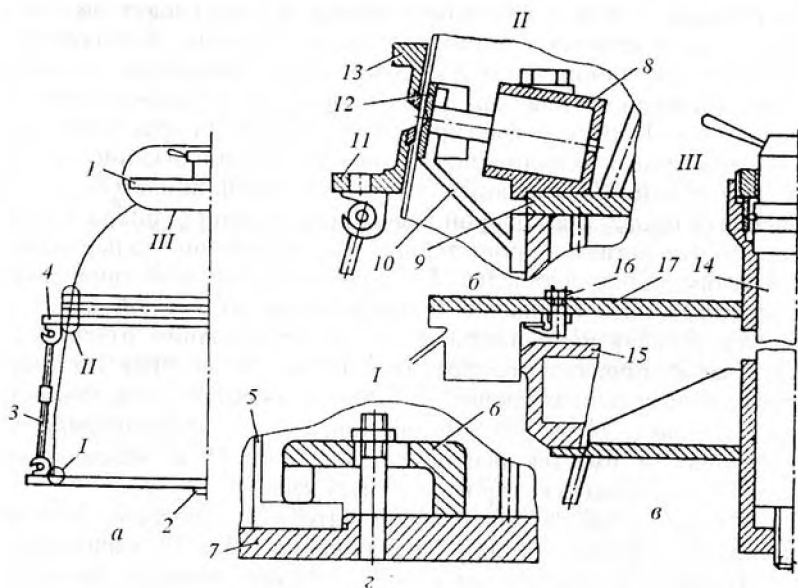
Схема приспособления для сборки-сварки сферической и конической оболочек корпуса СА
